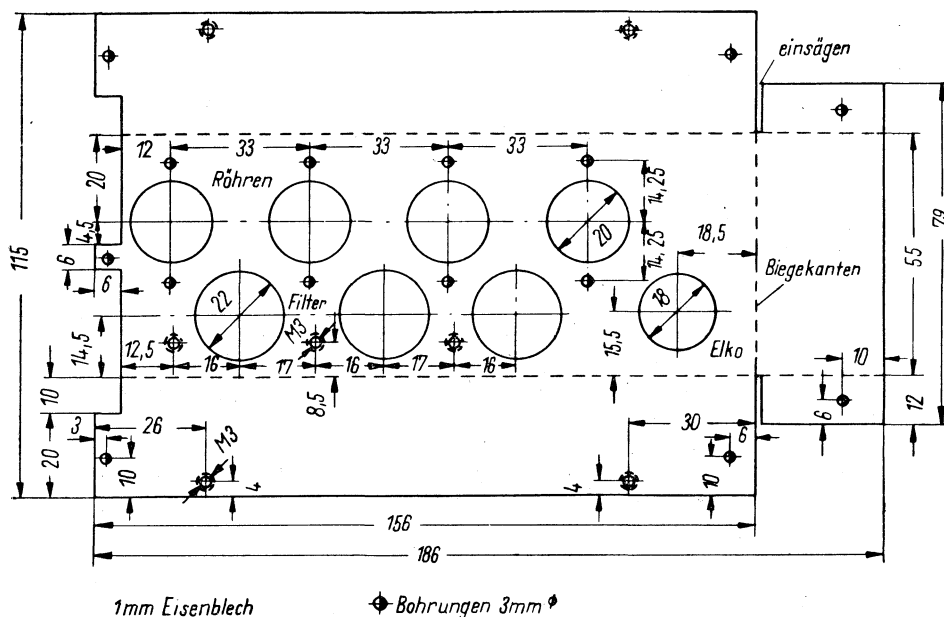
Maßskizze für das Chassis des UKW-Superhets
